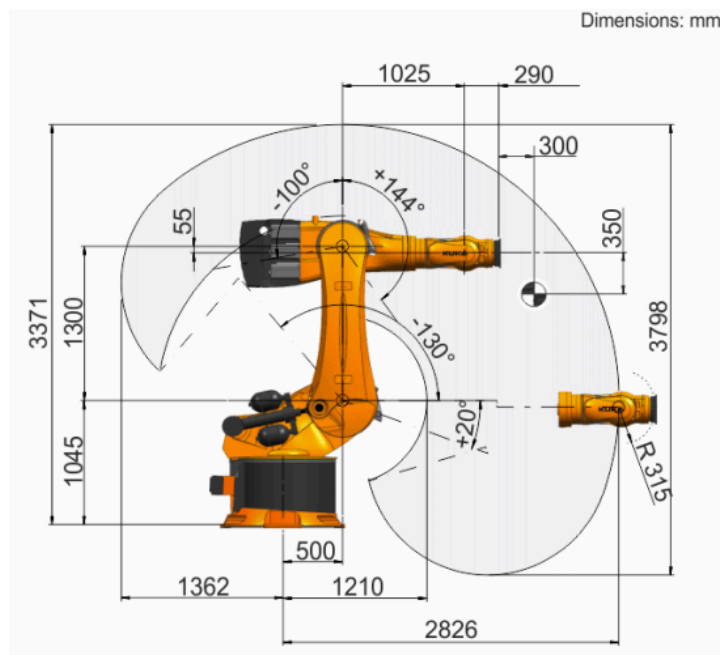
dimensiones y zona de trabajo del robot KR 600 R2830 del fabricante KUKA. Fuente: KUKA.
